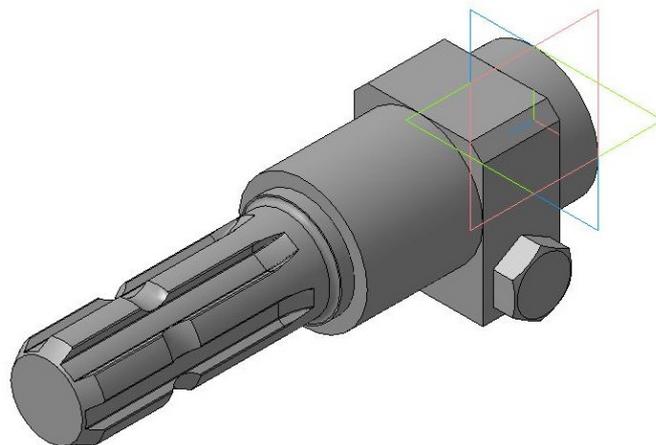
Механический привод мульчера навесной конструкции роторного измельчения
